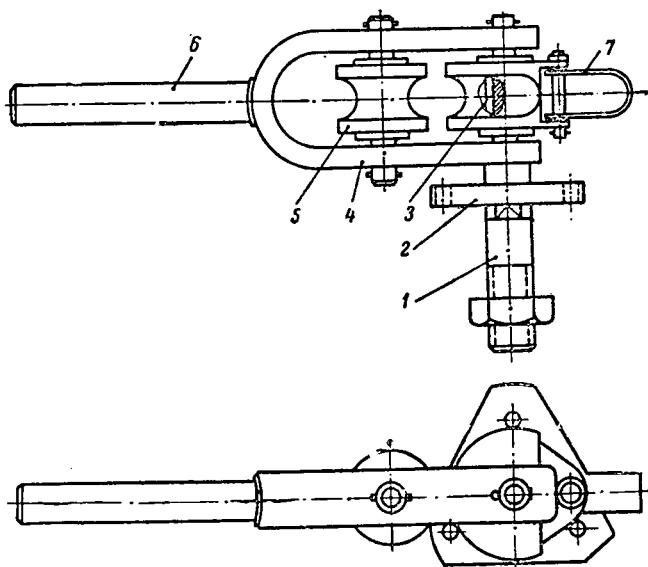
Ручной трубогибочный станок конструкции Вольнова
